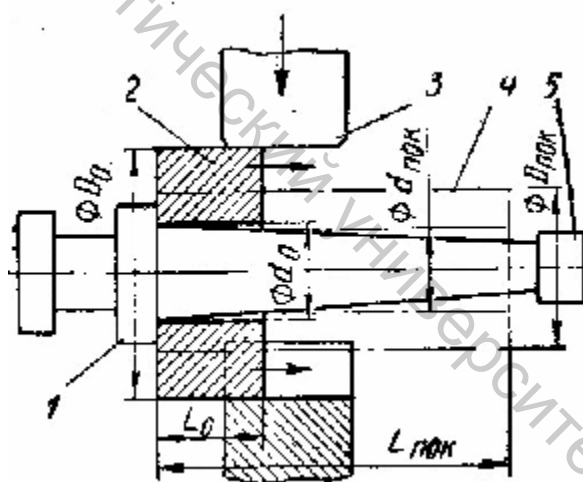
Схема протяжки с оправкой: 1— борт оправки, 2— заготовка, 3— боек, 4— поковка, 5— оправка
